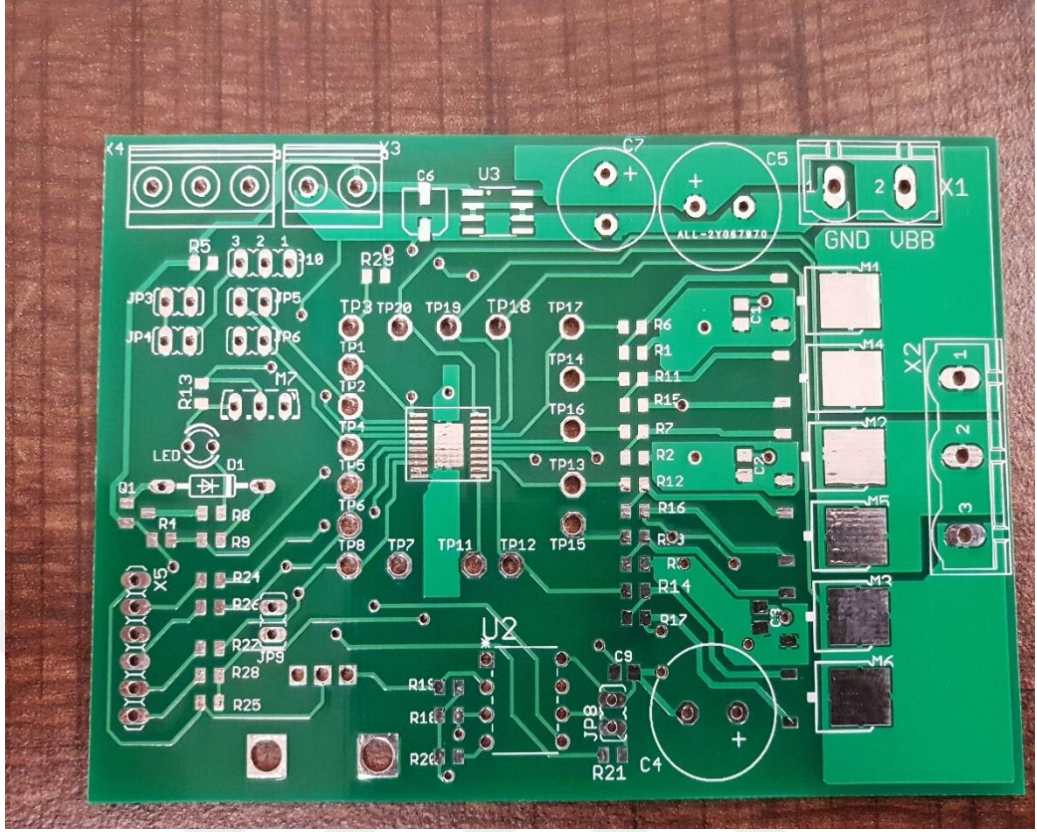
30 BLDC Sürücü PCB Üst Katman Çizimi
